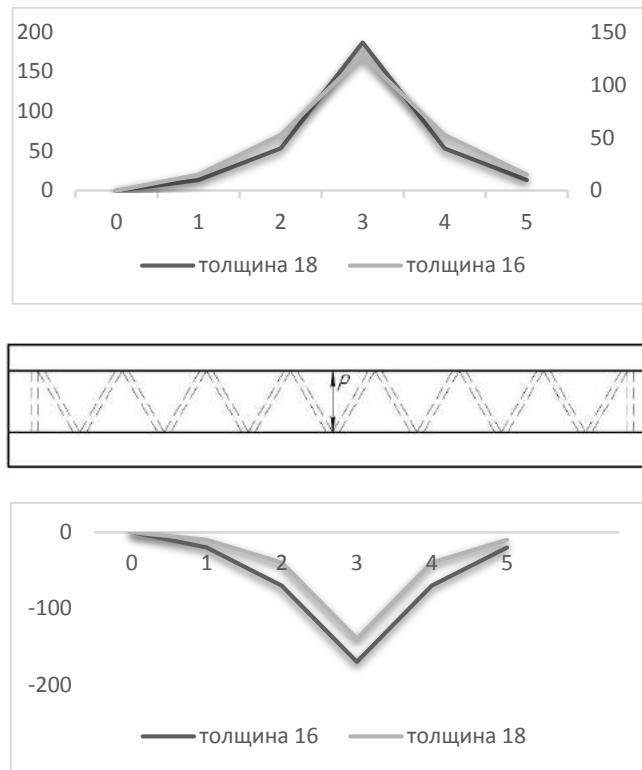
Розтискання полиць зварної станини верстата КЖ1910.
